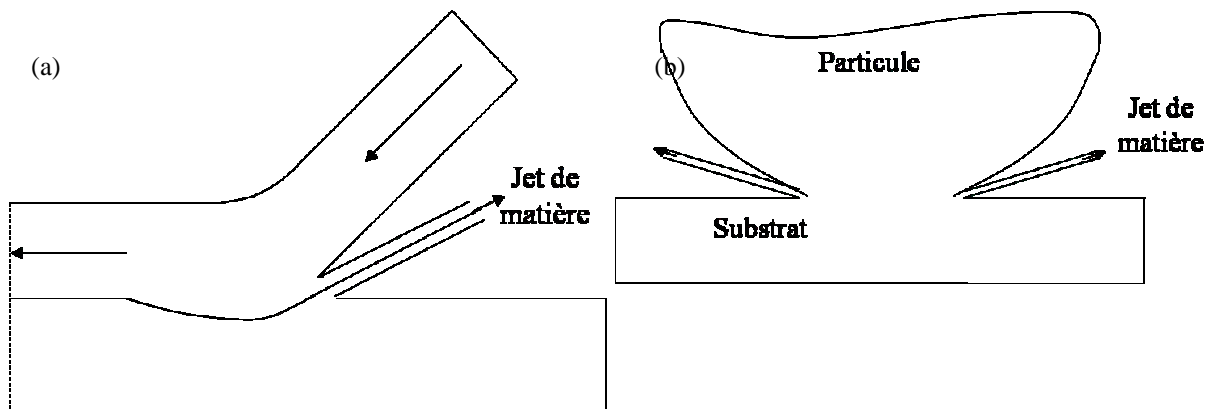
Schéma de l'éjection de matière en phase solide (a) lors du soudage par explosion de deux plaques [CRO82] et (b) lors de la projection par cold spray [JEA70]
